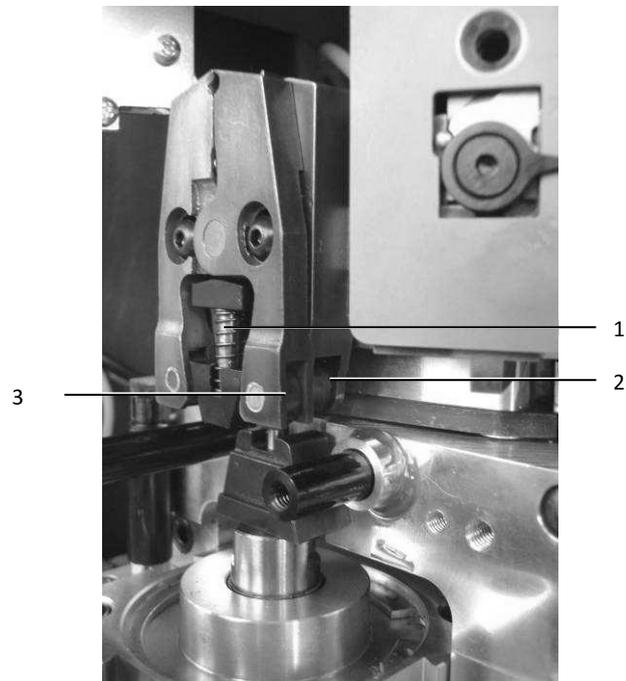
Hülsenhaltezange und Crimpwerkzeug
